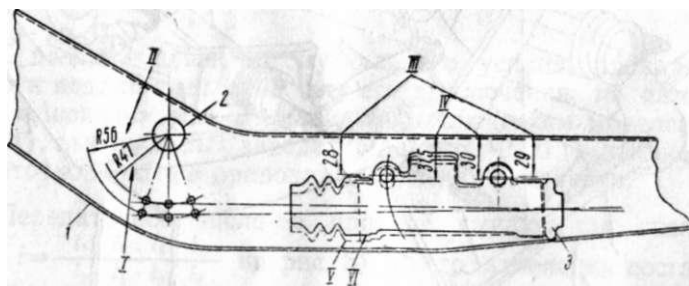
Положения отверстий на лонжероне рамы для прохода крепежных болтов корпуса главного тормозного цилиндра: / — лонжерон рамы; 2 — отверстие для прохода трубки оси педалей; 3 — корпус главного тормозного цилиндра; // — измененное положение отверстия на нижнем плече рычага педали; /// — прежнее положение отверстия на нижнем плече рычага педали; /// — положение смещенных отверстий в лонжероне; /V — прежнее положение отверстий в лонжероне; V — прежнее положение корпуса главного цилиндра; VI — измененное положение корпуса
